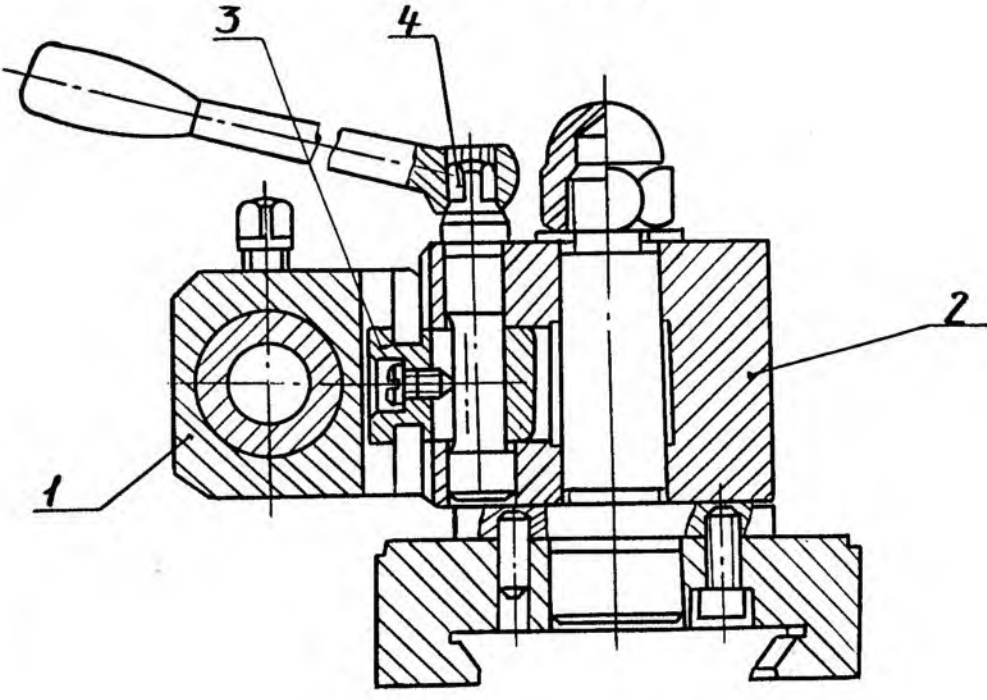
Двухпозиционный неповоротный резцедержатель с быстросменными блоками.
